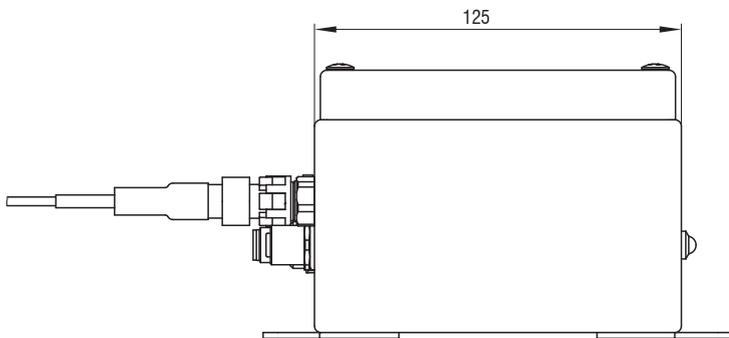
Maßzeichnung Frontansicht des IMC5420IP67 Controllers, Abmessungen in mm (Zoll)
